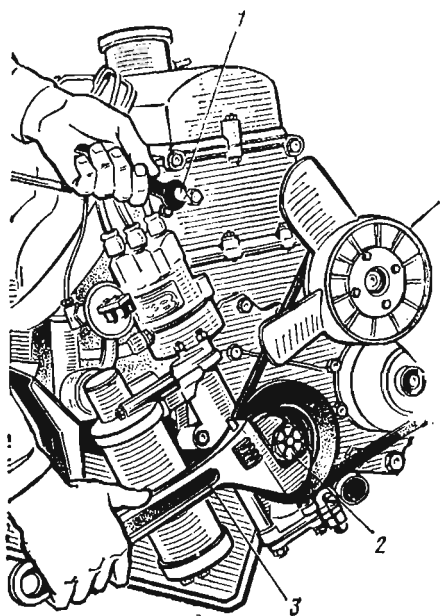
Регулировка натяжения цепи привода распределительного вала
